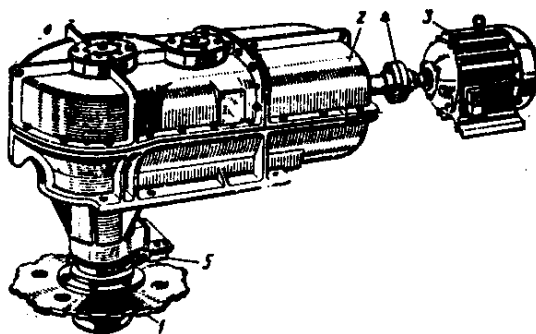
Кутовий привод з редуктором типу ВДВ
